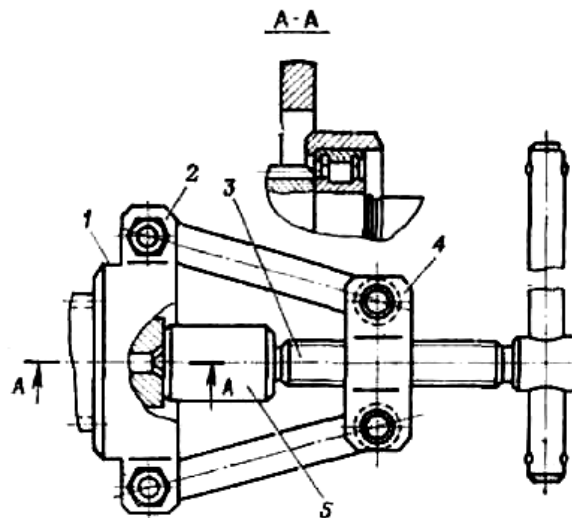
Знімач переднього підшипника ведучого вала: 1 - захват I-801.30.200; 2 - гайка; 3 - гвинт; 4 - траверса; 5 - наконечник
